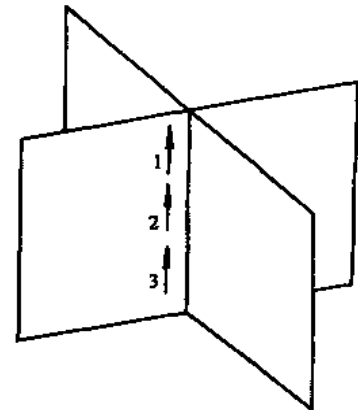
框架间立角焊缝向上立焊分段退焊法
